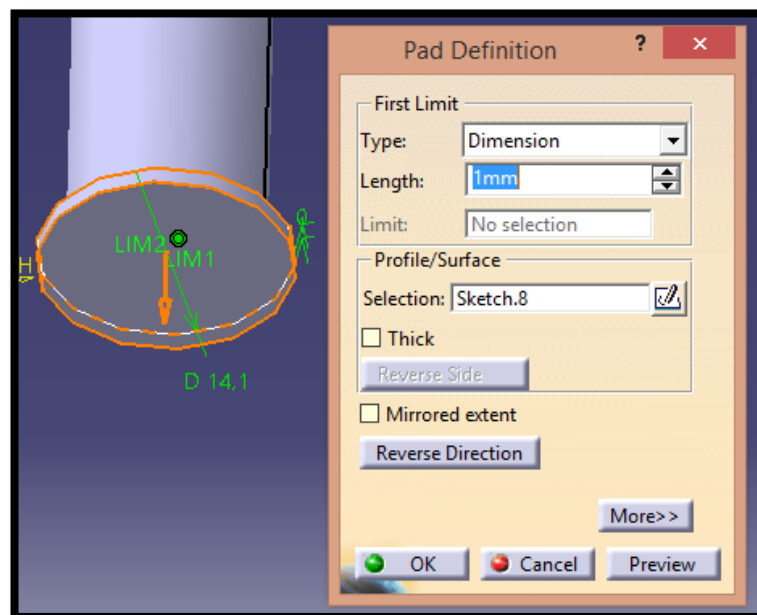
Seat mounting frame 11: Pad.2 pestillo superior 2
